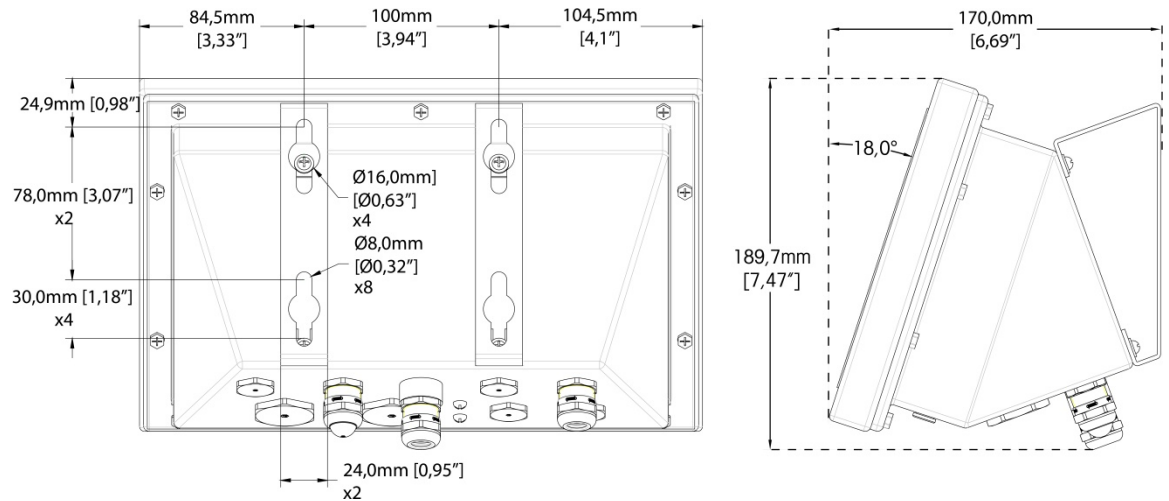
Dimensiones de la caja para ambientes adversos del IND570xx con soportes de montaje de ángulo fijo, montaje VESA
